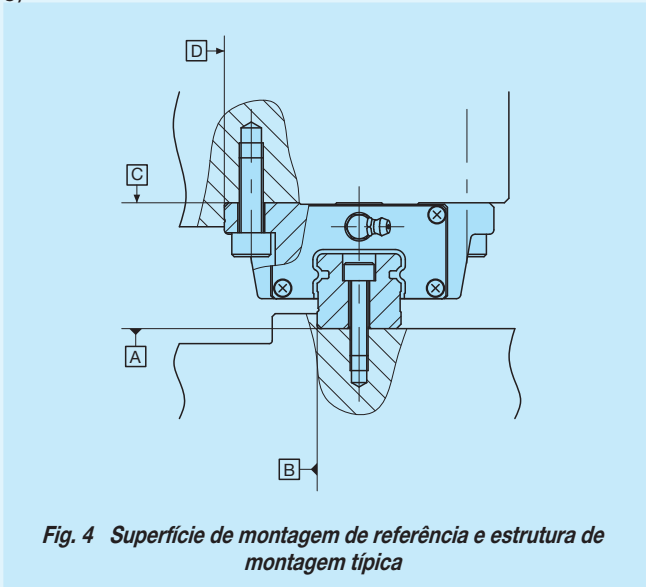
Superfície de montagem de referência e estrutura de montagem típica
